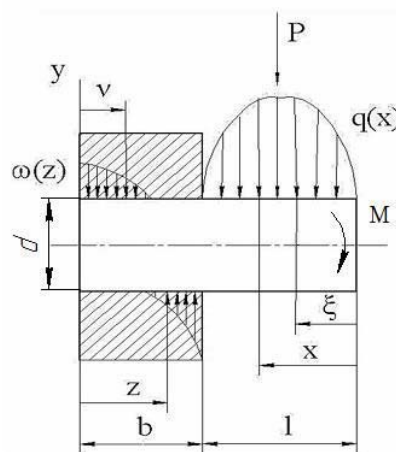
Схема нагружения оси шестерни и щеки корпусной детали
